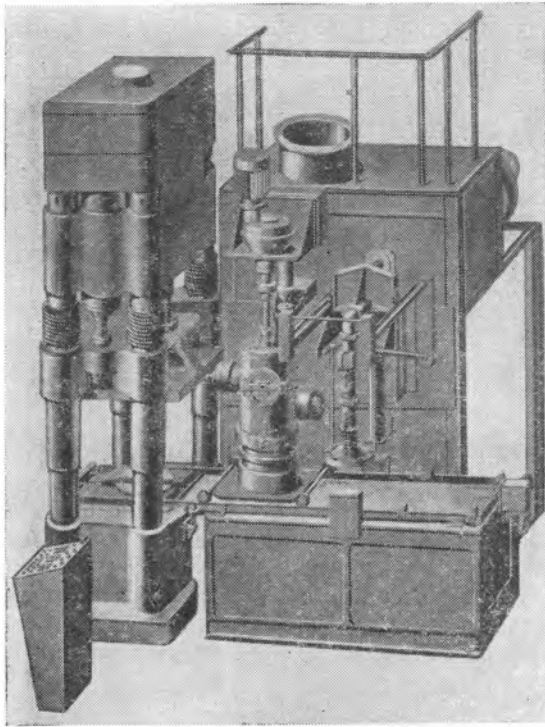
Механизированный пресс ФА-315-350М для формования мелкозернистых изделий диаметром 250—350 мм
